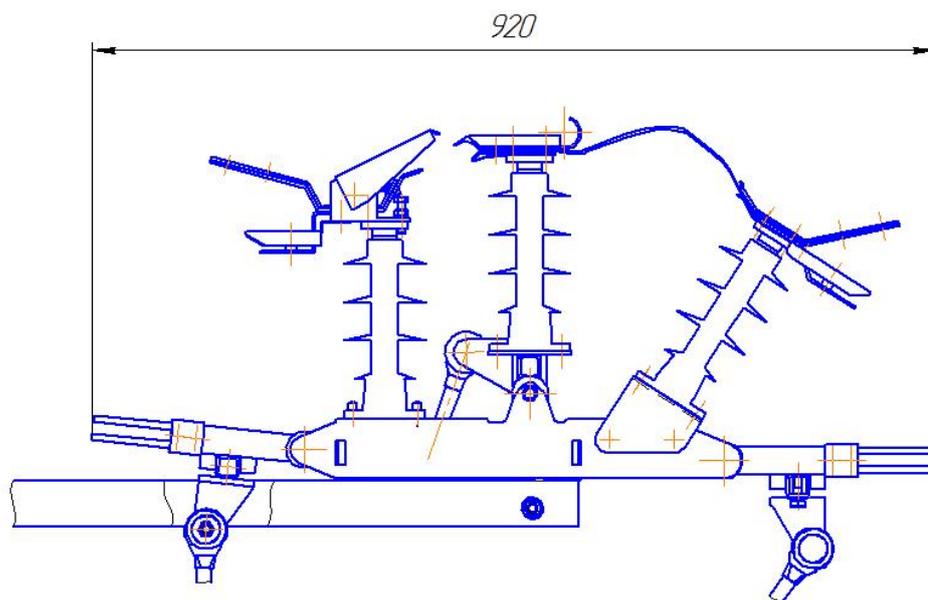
Разъединитель типа Р/К-10 IV/400УХ/11 с приводом типа ПР-7УХ/11
